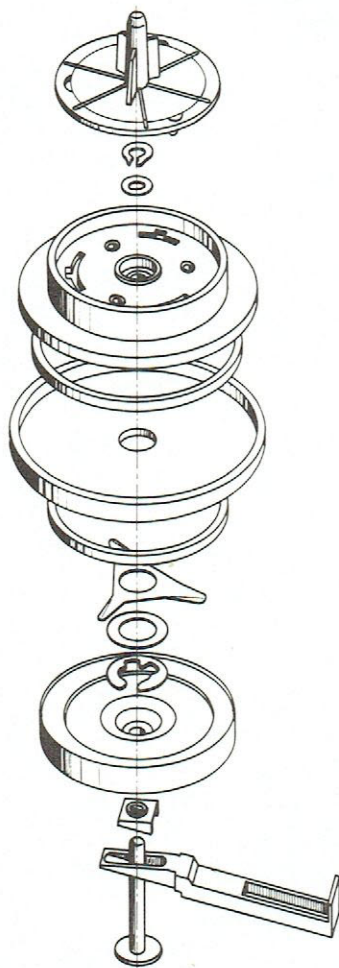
Vue éclatée du plateau de rebobinage gauche
